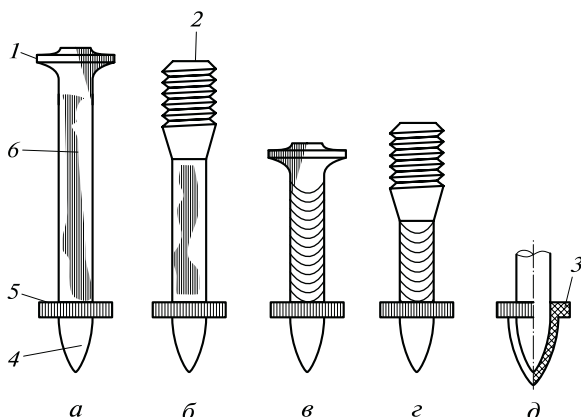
Дюбеля к строительно-монтажному пистолету ПЦ-52-1:
